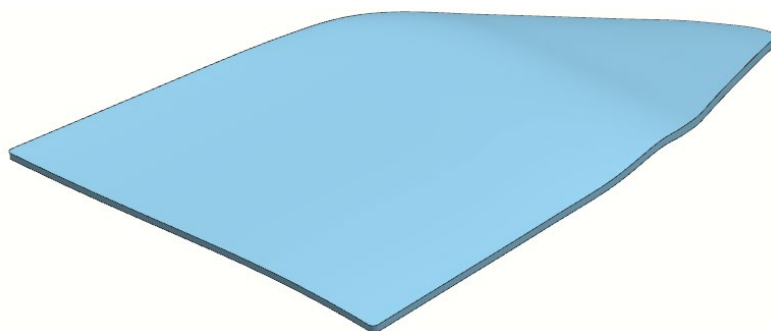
Оптимизированная CAD модель детали «Обшивка»
